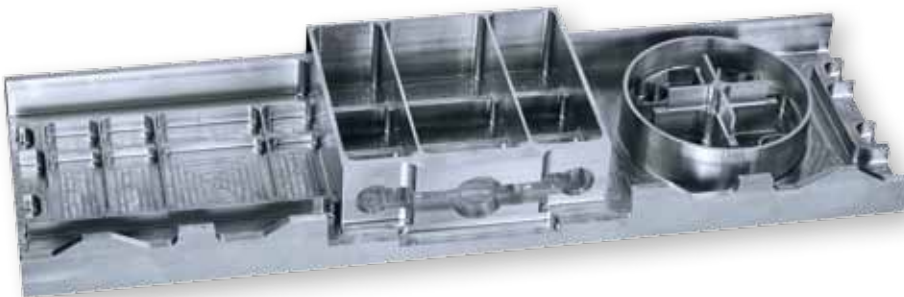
FRAISA ToolSchool 加工案例航空铝3.4364 (7075)
